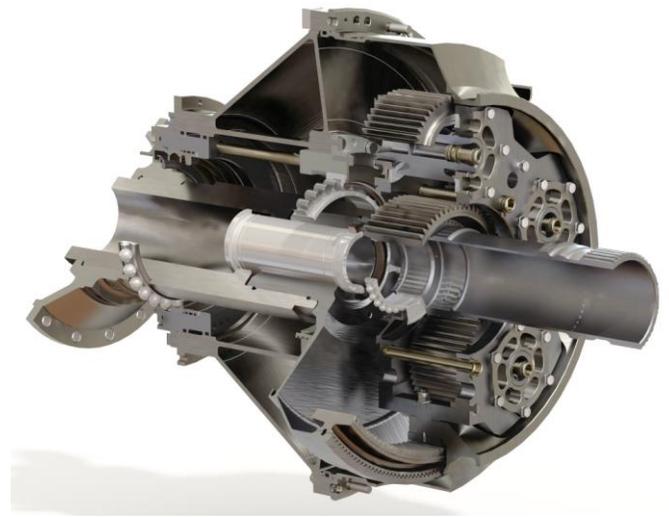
Редуктор привода вентилятора авиационного двигателя нового поколения
